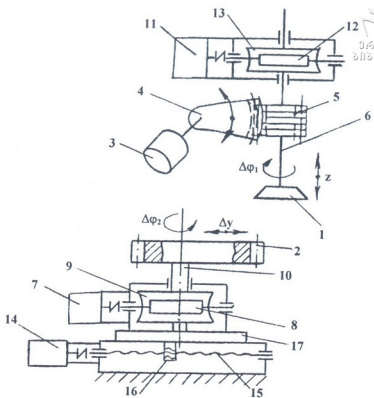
Схема нарезания некруглого цилиндрического колеса с наружными зубьями с применением
